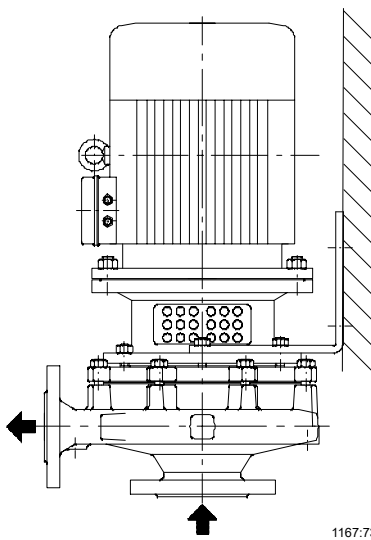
Pumpenfuß Befestigung seitlich, bis Motorgröße
